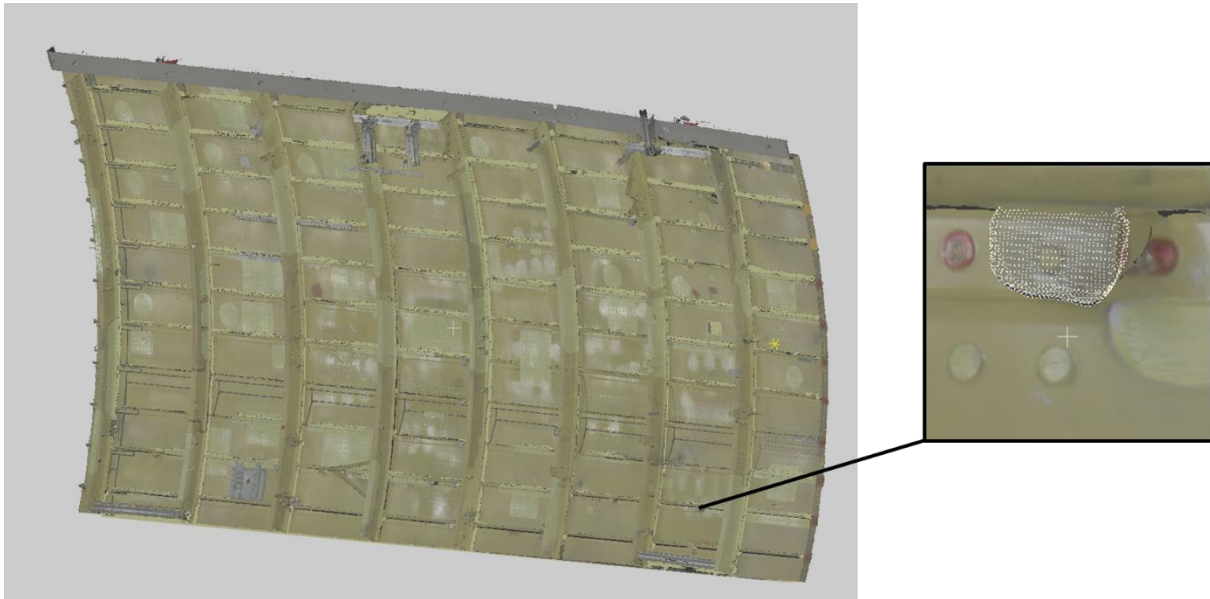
Aufgenommener Gesamtscan und beispielhafter Detailscan eines Halters
